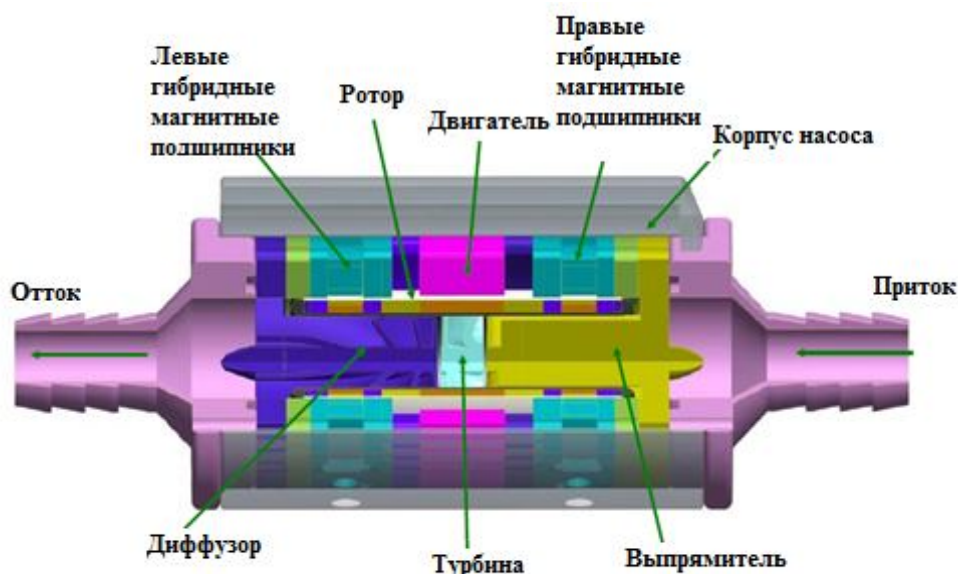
Сердечный насос с гибридными магнитными подшипниками [12]
